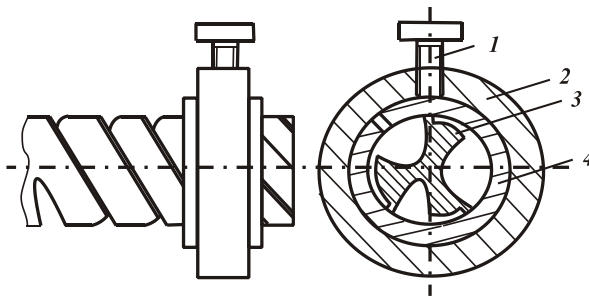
Схема доведення зовнішньої поверхні твердосплавного багатолезового інструмента: 1 – гвинт; 2 – кільце; 3 – оброблювана деталь; 4 – притир [20]
